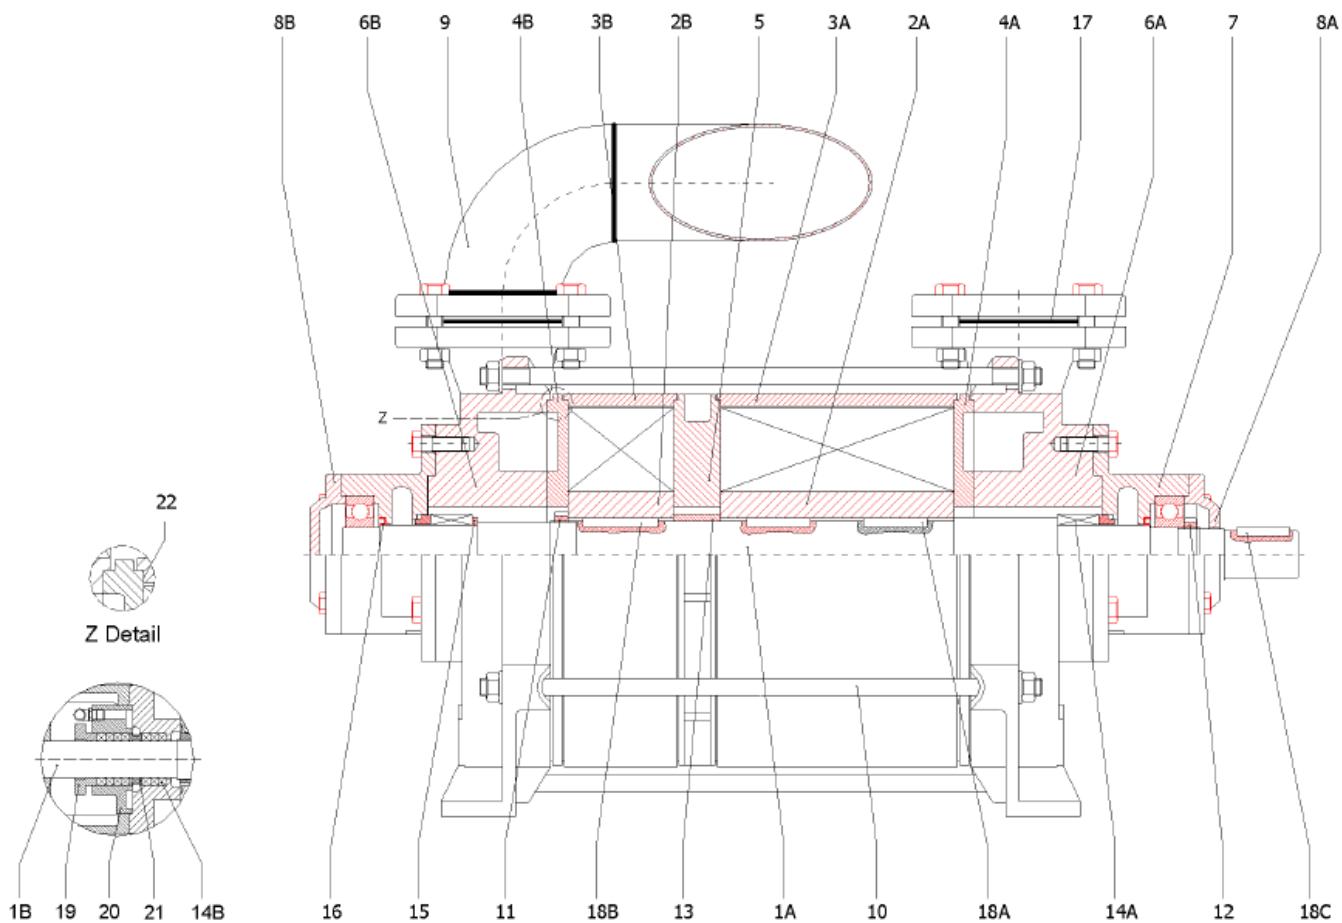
Сборочный чертеж GVP 200, GVP 230, GVP 275
